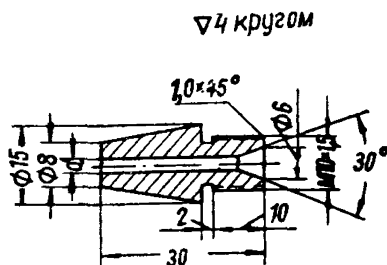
Переходная втулка к держателю для полуавтоматической сварки стыков арматуры
